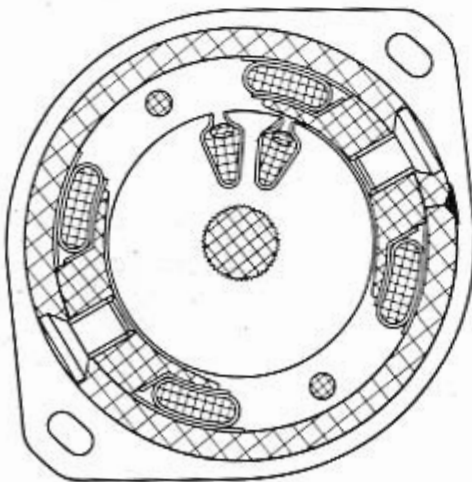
Coupe transversale sur l'induit et sur les épanouissements polaires.
